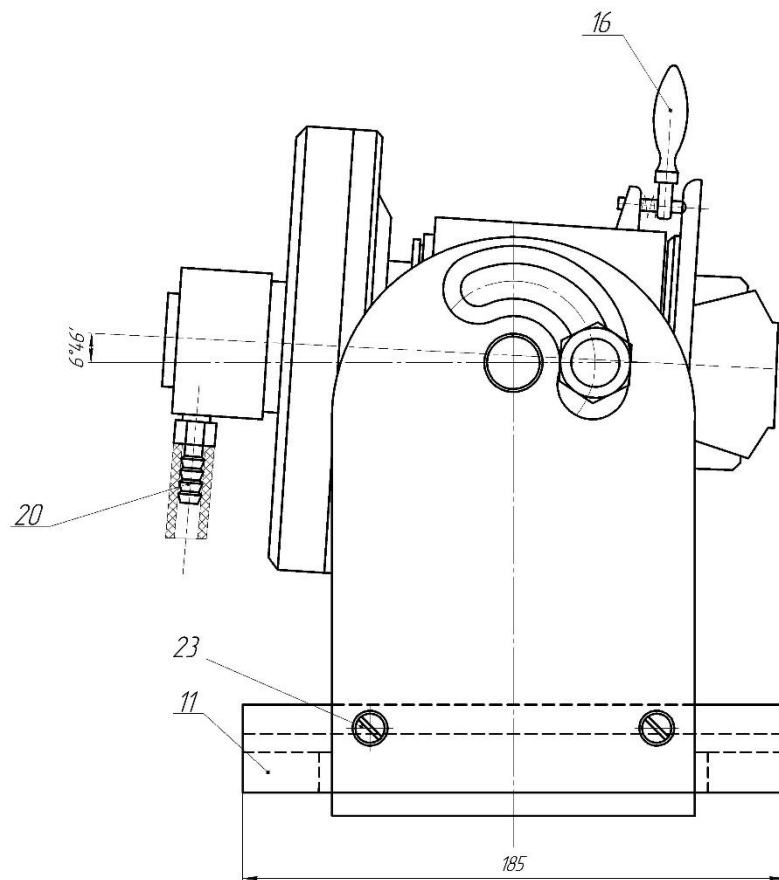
Пристрій для фрезерування пазу під багатогранну пластину
